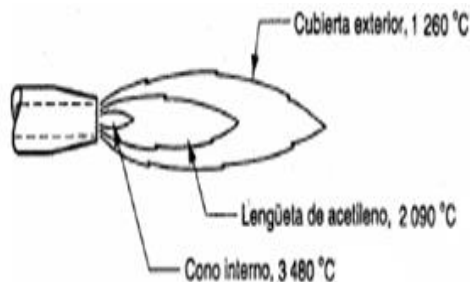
Tipos de llamas empleadas en el proceso de soldadura oxiacetilénica.
